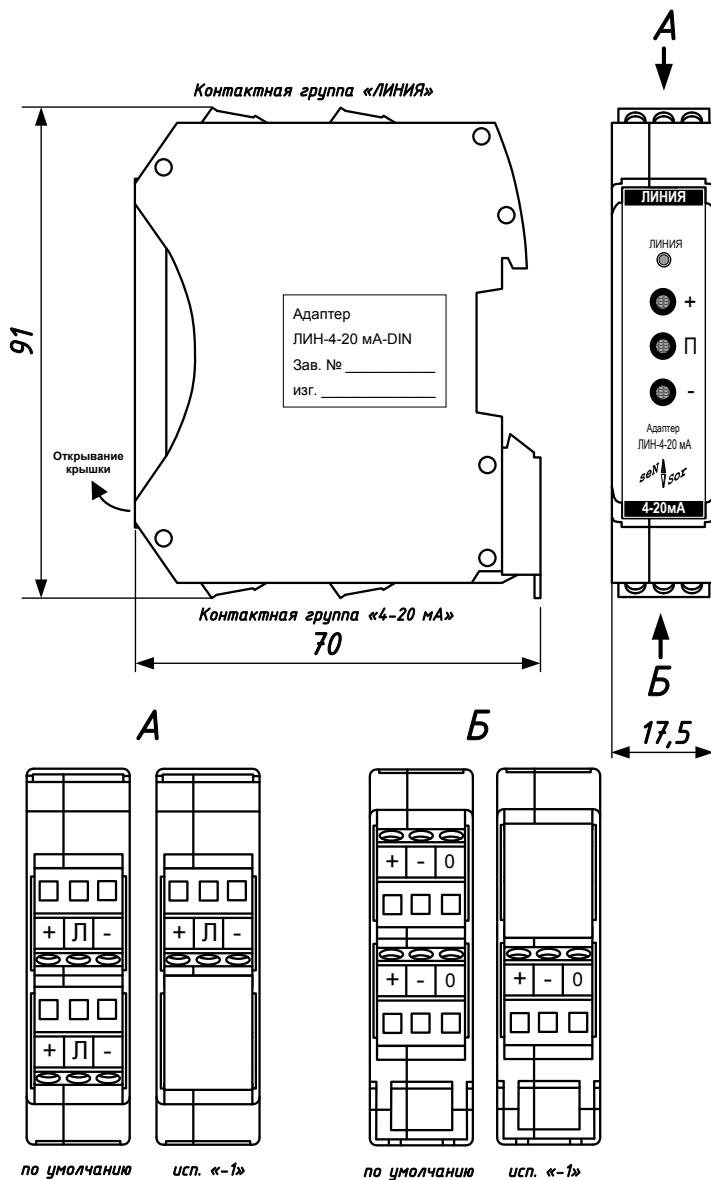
Адаптер. Внешний вид, габаритные размеры.
